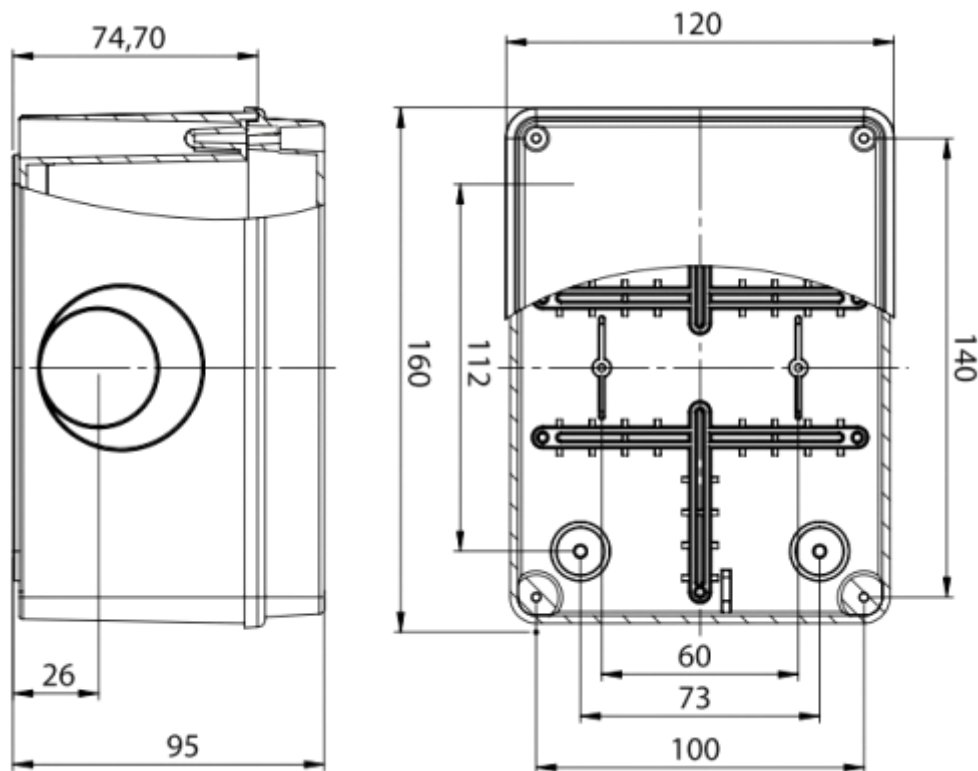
Вид, размеры корпуса АБРМ.301129.30–02 для ЭМ А80–2
